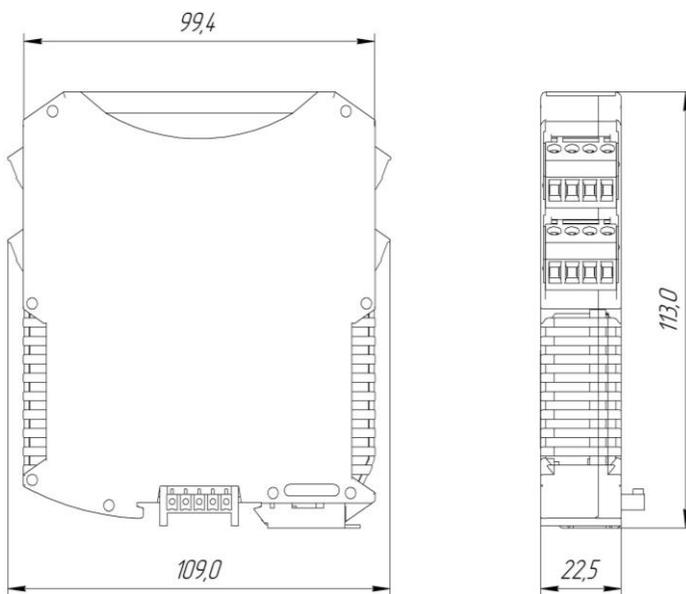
Габаритный чертеж модуля NLS-DM-60
